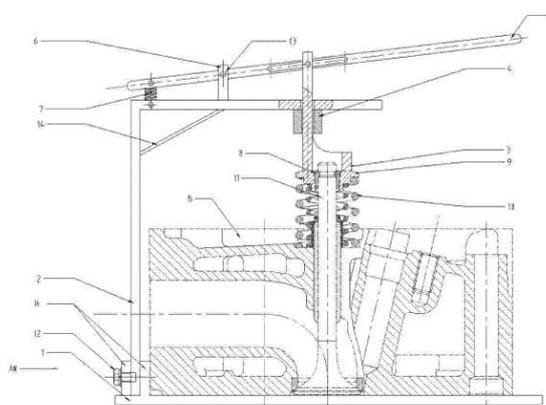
CN 203752093 – Special tool for detaching and installing valve spring of diesel engine.
